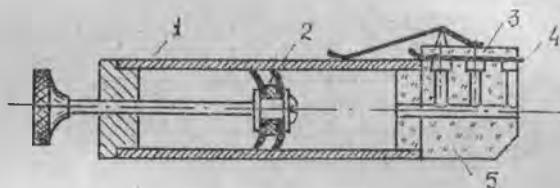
Конструкция прибора ПОЗ-Т: 1 — корпус; 2 — поршень; 3 — замок; 4 — фильтрующий элемент; 5 — датчик
